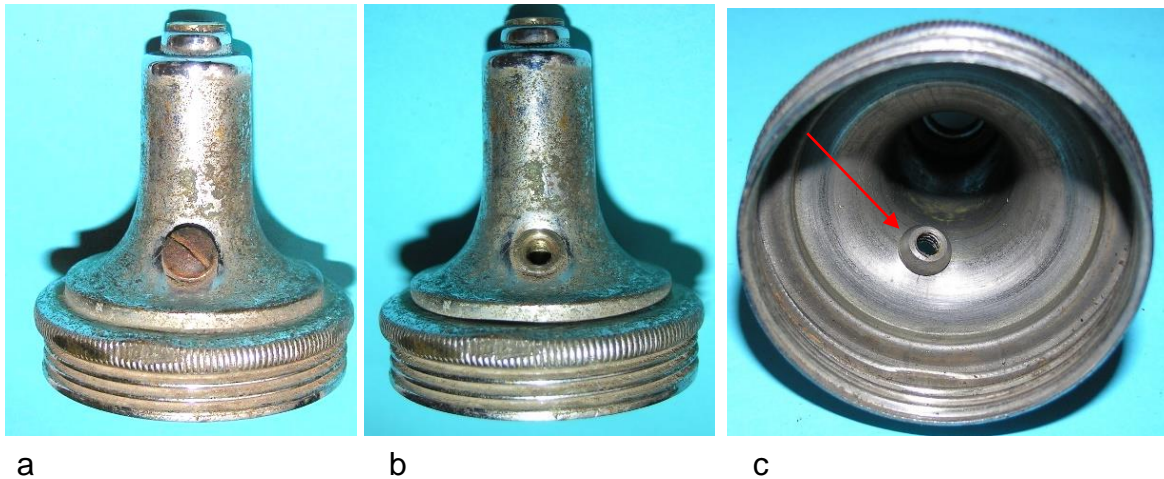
Ölbohrung im Lagerhals: a) Verschluss mit einer Schlitzschraube, b) Umbördelung des Gewindeeinsatzes, c) Innenansicht des Gewindeeinsatzes
